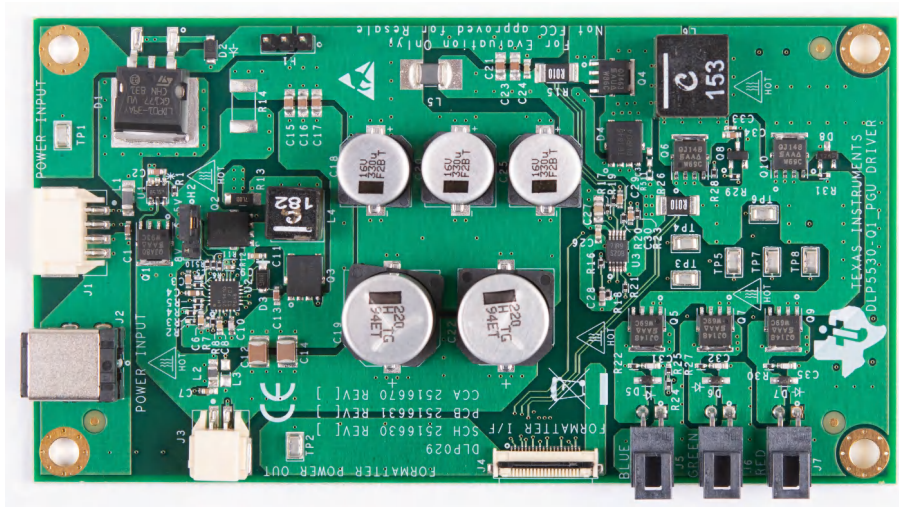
DLP5530PROJTQG1EVM 照明ドライバ PCB
